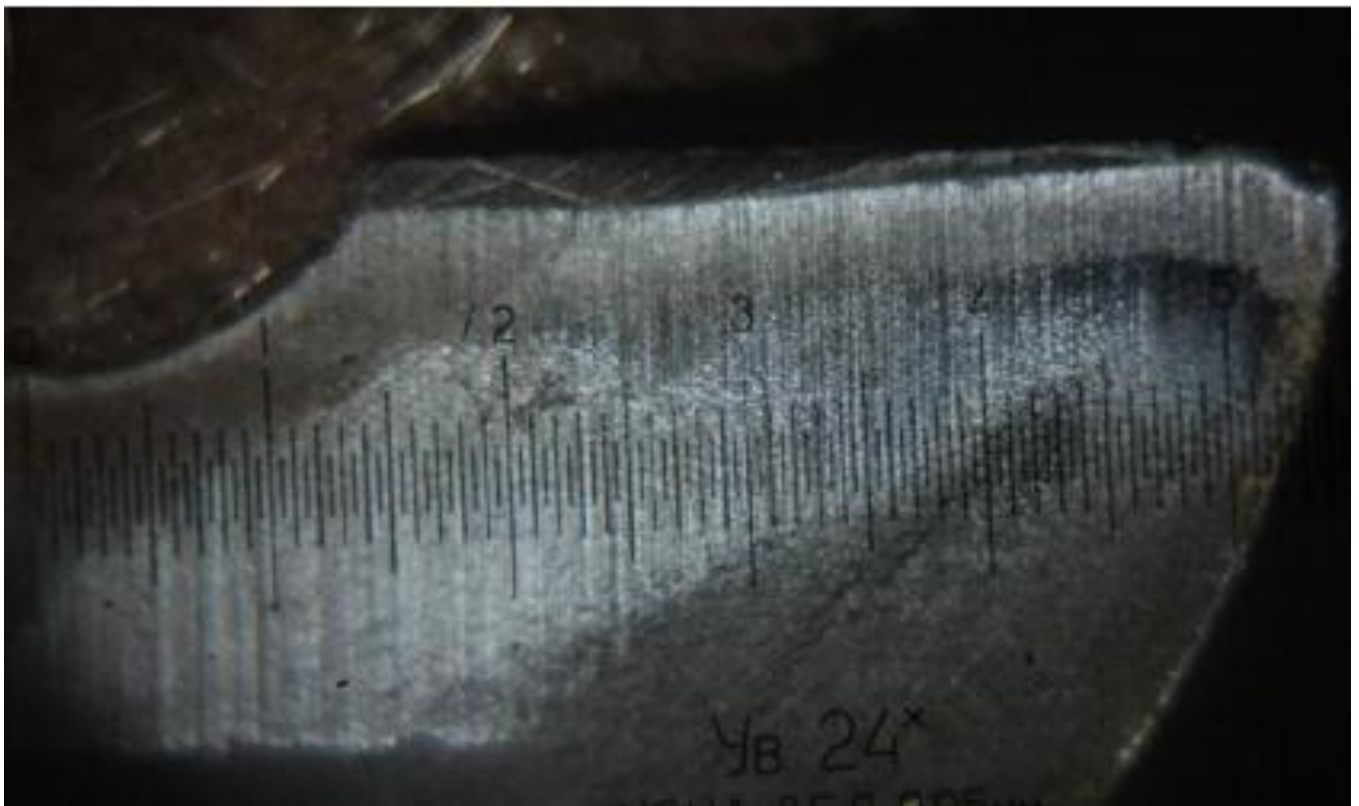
Абразивний знос інструменту по задній поверхні
